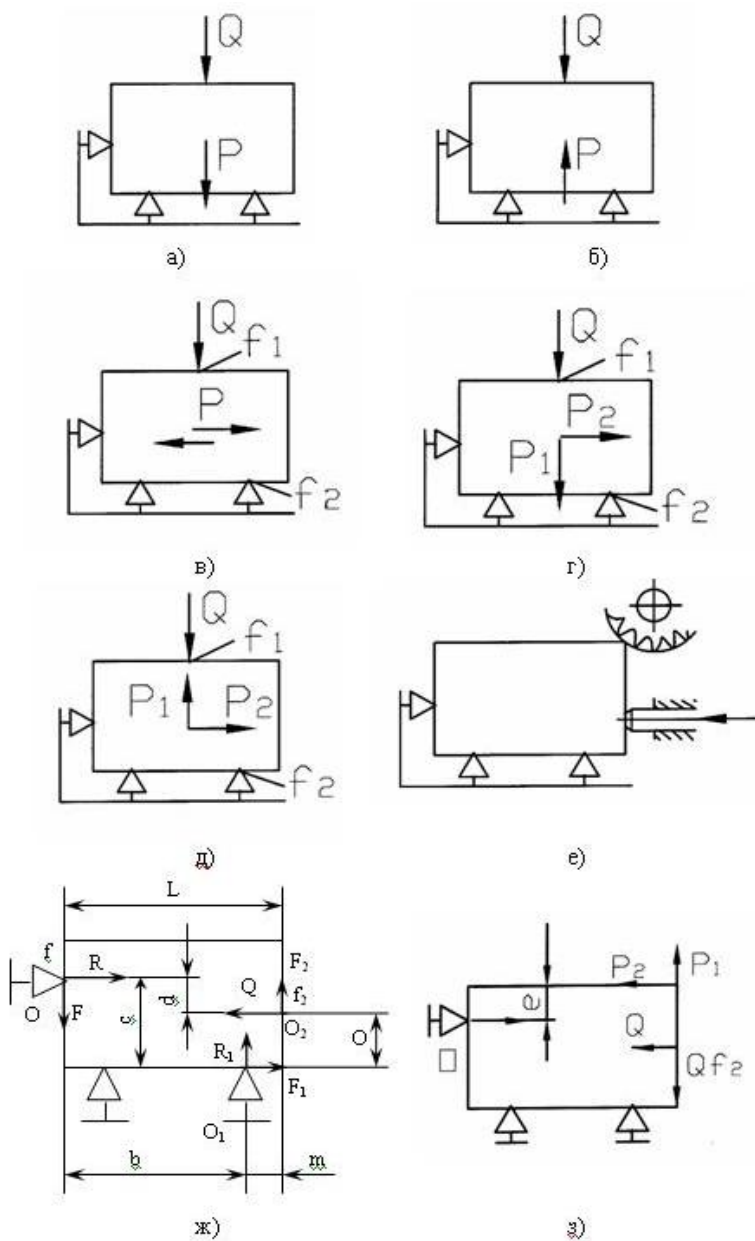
Схемы для расчета сил закрепления заготовки
